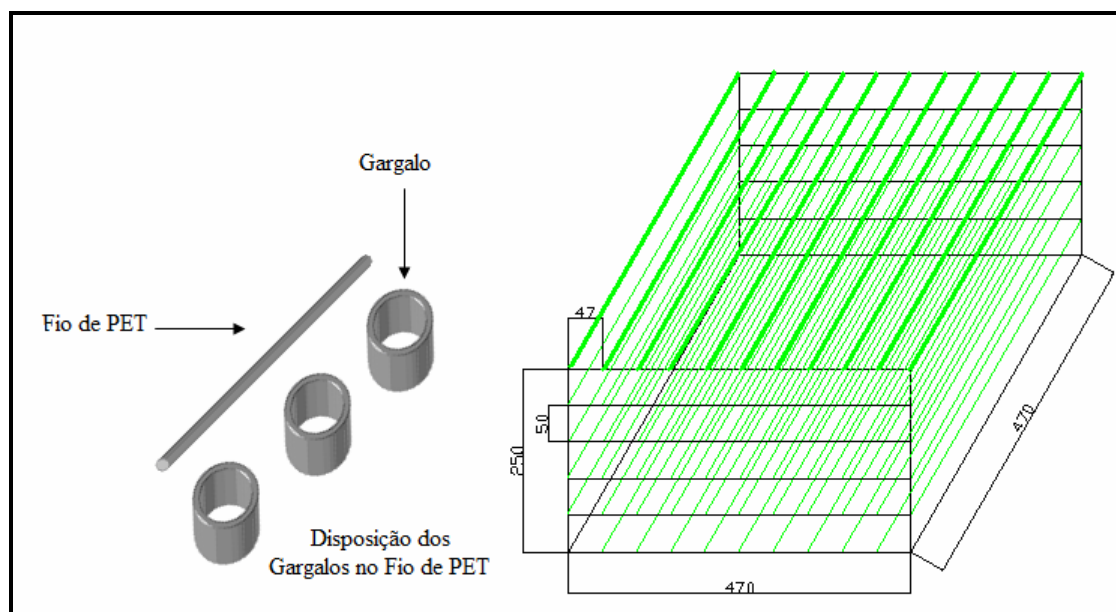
Caracterização do enchimento fio cruzado.
